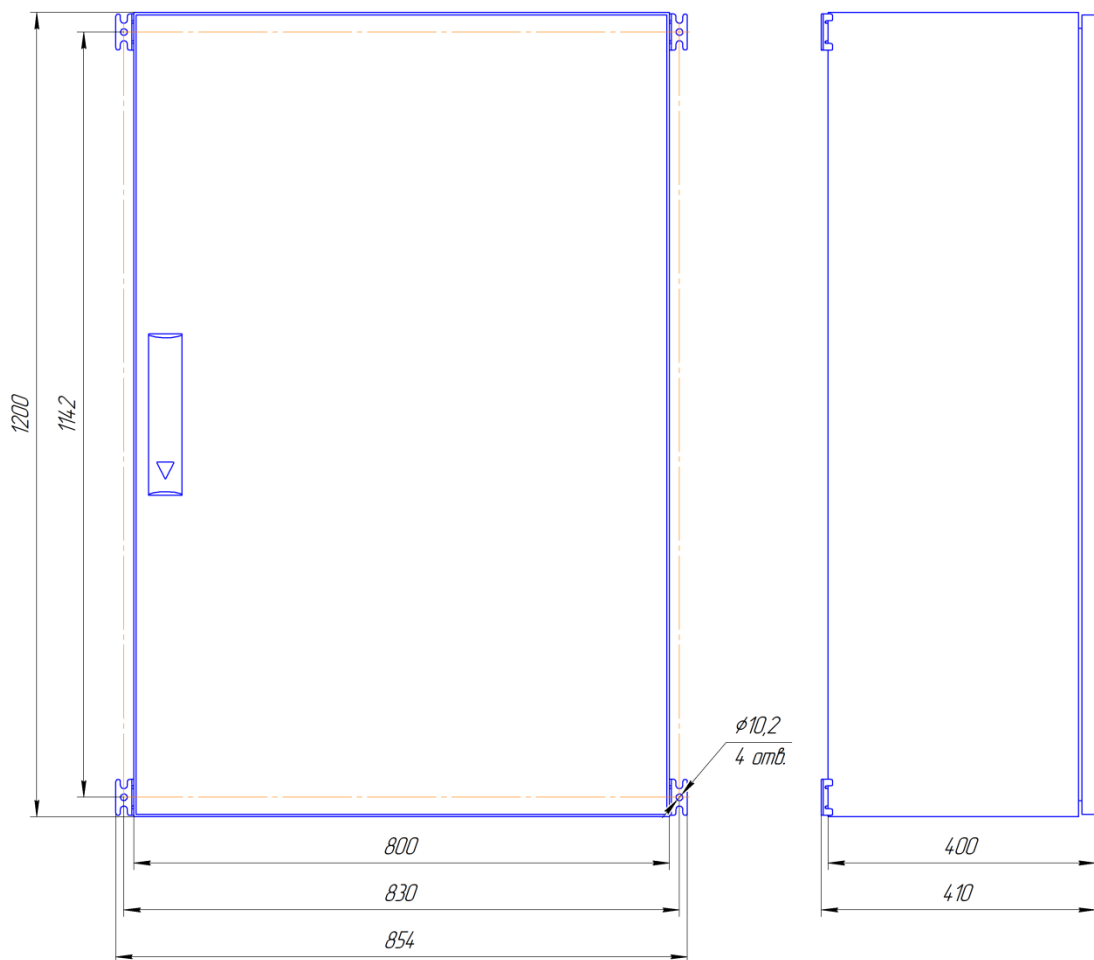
Габаритные и установочные размеры настенного шкафа
